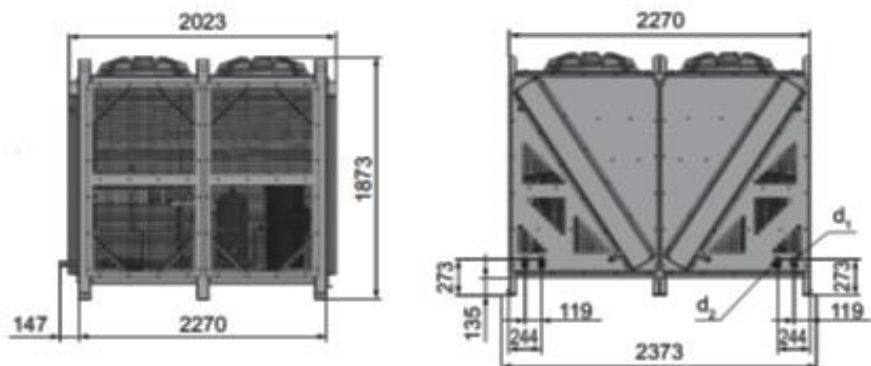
Загальний вид агрегату типу МАКК-120-1251, МАКК-120-1562
